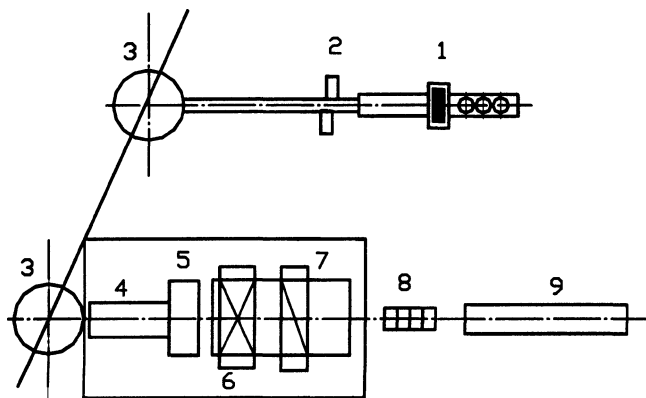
Сортовой стан бесконечной прокатки завода Такамацу фирмы «Tokyo Steel»: 1 – двухручьева МНЛЗ для отливки заготовок диаметром 200 мм; 2 – устройство огневой резки; 3 – поворотные устройства; 4 – входной рольганг; 5 – устройство гидросбива окалины; 6 – сварочная машина; 7 – гратосниматель; 8 – индукционный подогреватель; 9 – черновая группа клетей
